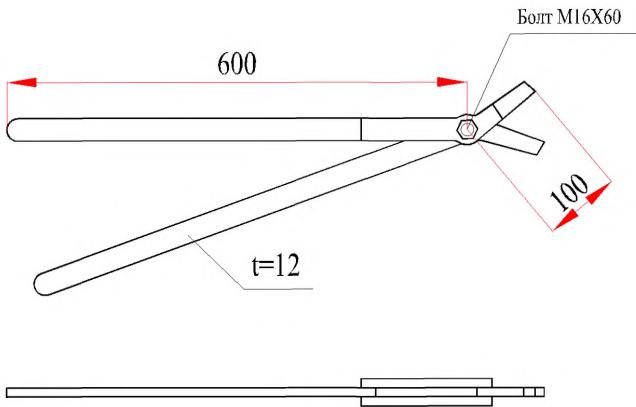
Приспособление для сборки трубы фундамента со стойкой промежуточной опоры
